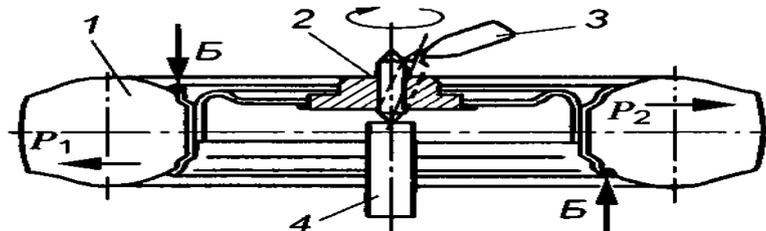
Динамическая балансировка колеса: 1 - колесо; 2 - приспособление; 3 - мел; 4 - опора.
